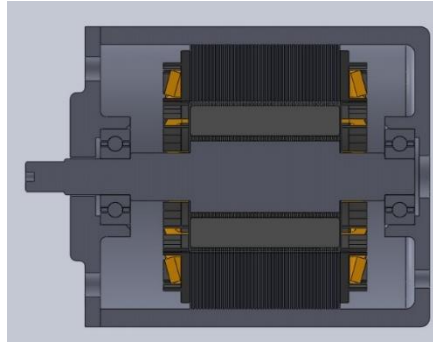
Statorun motor gövdesine geçirilmesi
